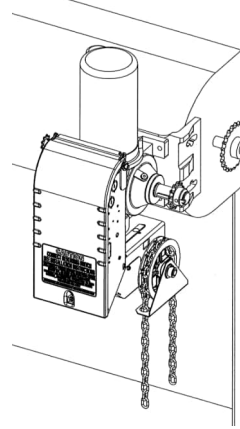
Montaje de pared lado izquierdo con BRACKET111 (polea de cadena a la derecha)
